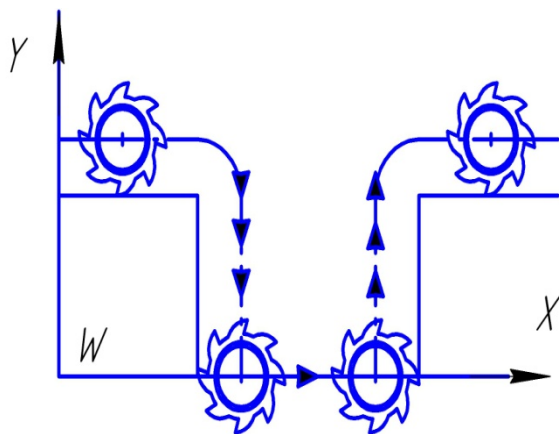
Контур, обработанный фрезой большого диаметра
